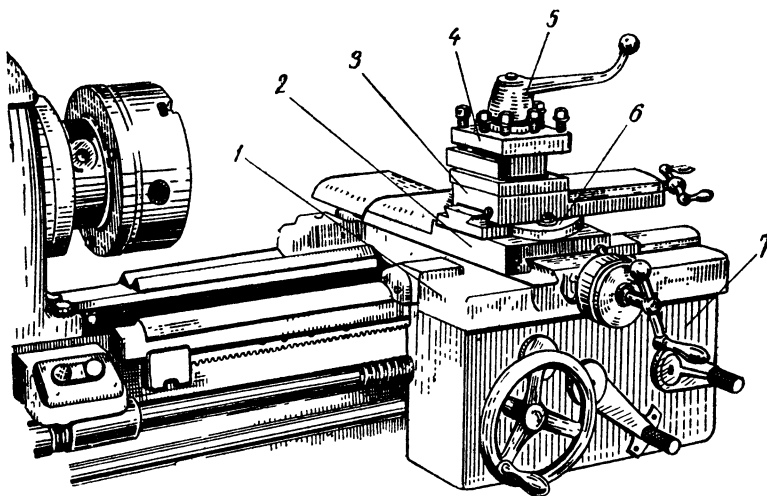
Суппорт токарно-винторезного станка модели 1615-М.
